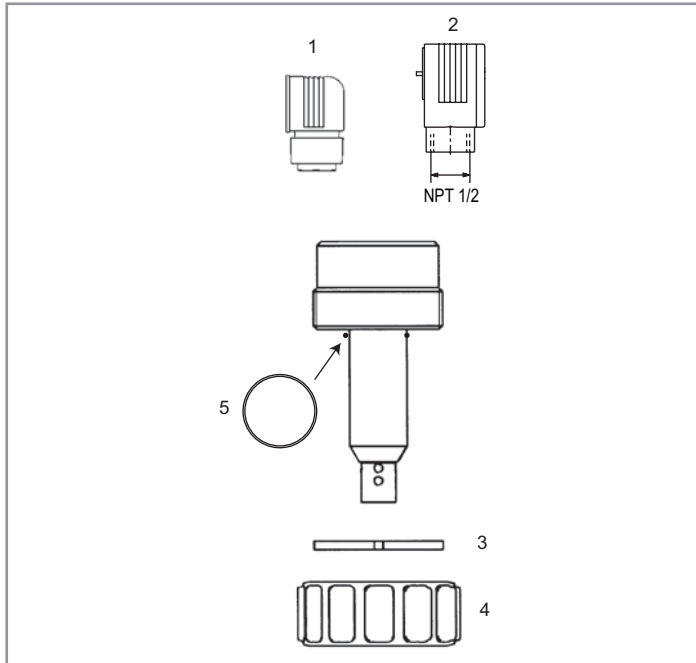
Explosionszeichnung des Leitfähigkeitssensors Typ 8220
